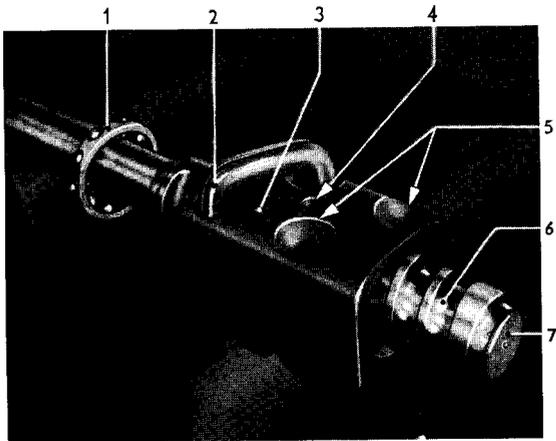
Hinterer Kugelkreislauf mit Kugelführungsrohr geschlossen
